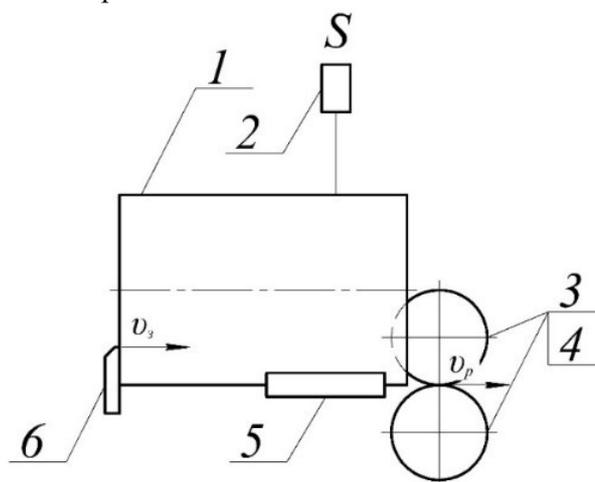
Схема прохождения заготовки через узел сварки
